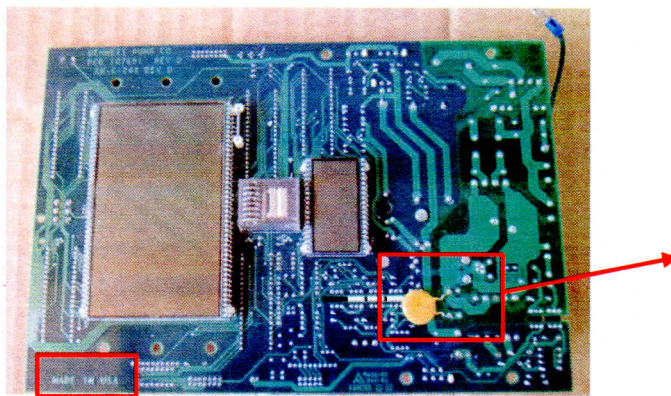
Detalle de Varistor, Vista Cara de Soldaduras.
